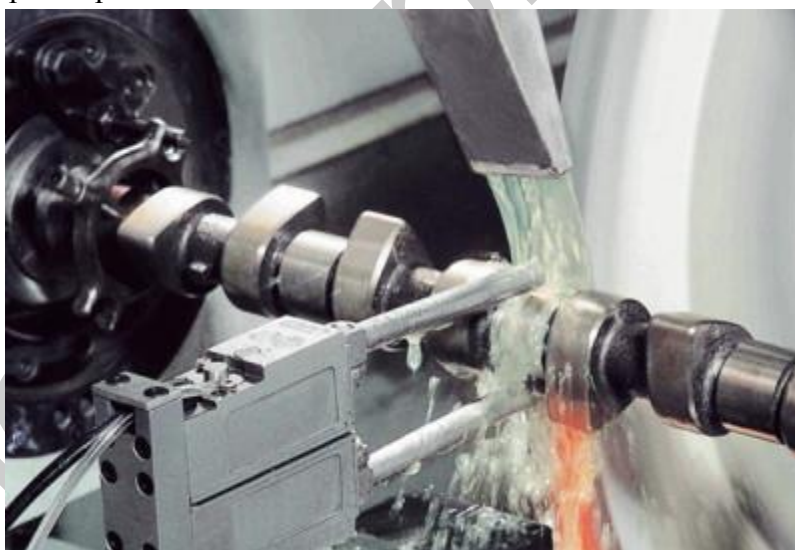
Пример обработки на станке с ЧПУ, содержащий сервопривод
